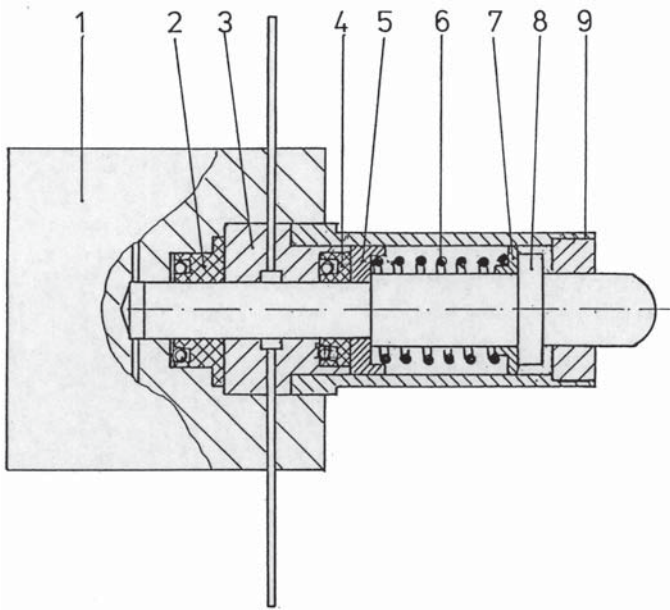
Pumpenkopf-Kolben-Querschnitt
